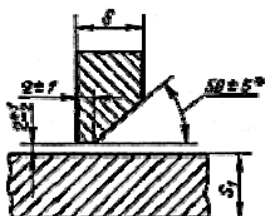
Сварное соединение Т7 по ГОСТ 8713-79
